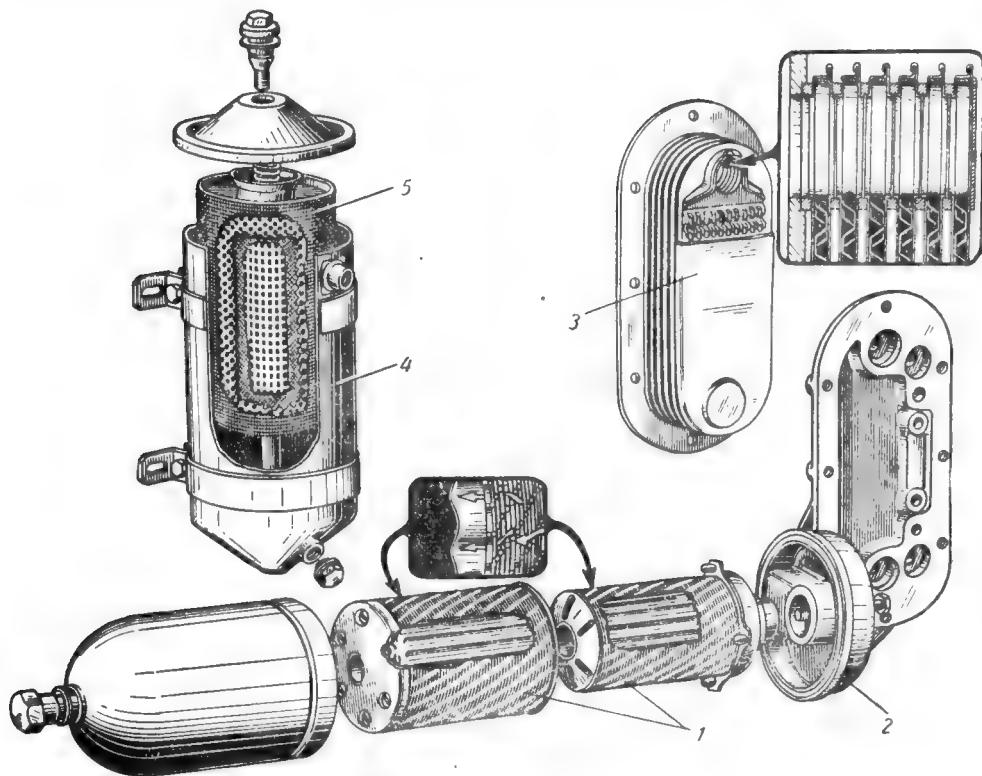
Схема системы смазки двигателя ЯАЗ-204.
